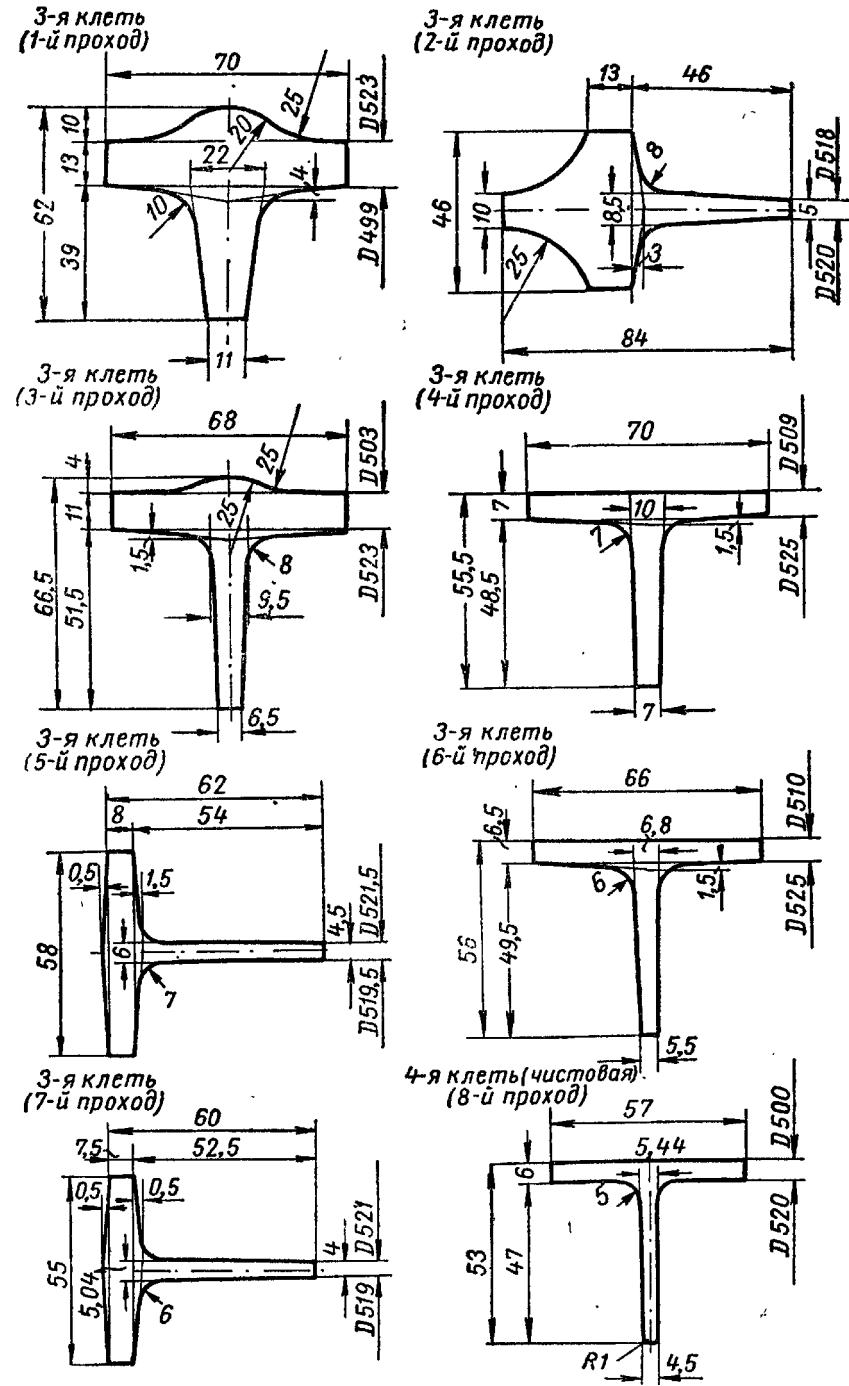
Размеры шаблонов для прокатки тавровой стали 56×52×6×4 мм на стане 500
